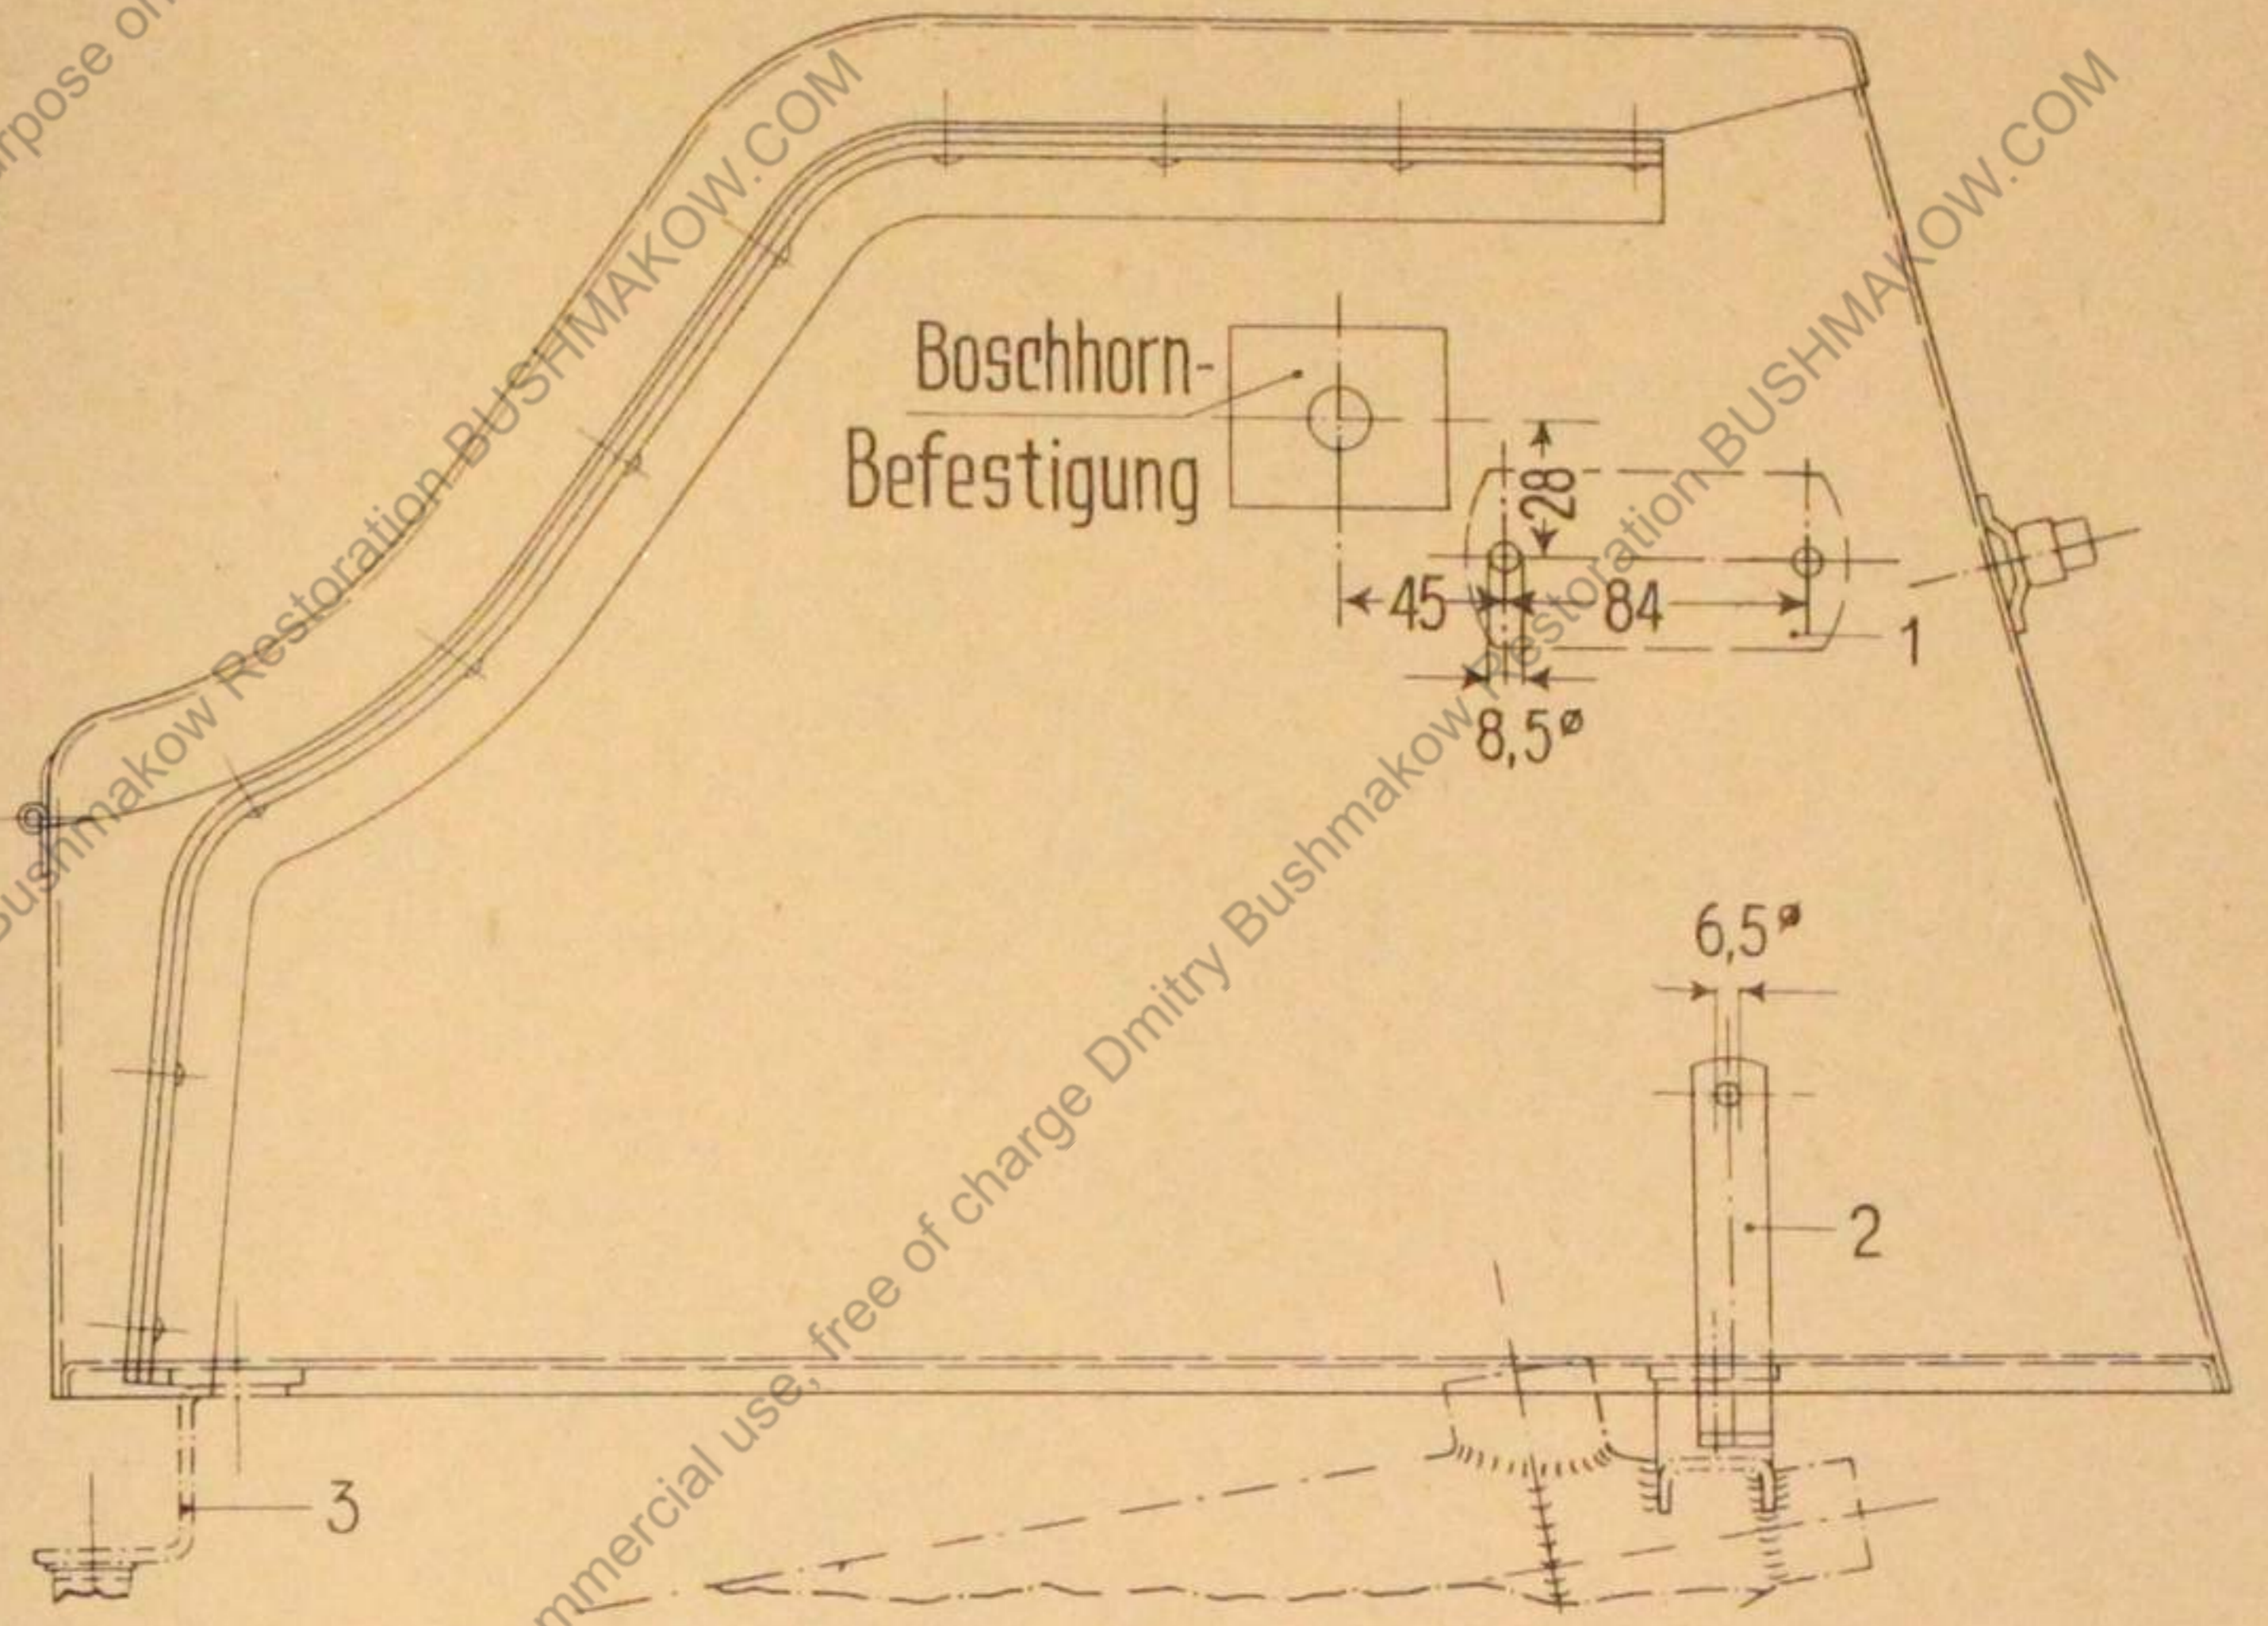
Einbauskizze für Halterbefestigung zum Anlaßkraftstoffbehälter
